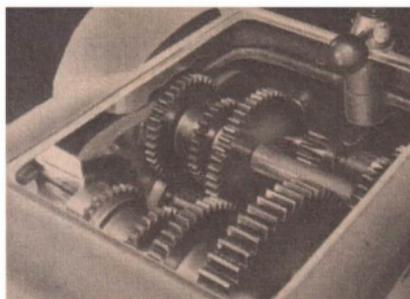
/1 Zahnradgetriebe einer Drehmaschine
